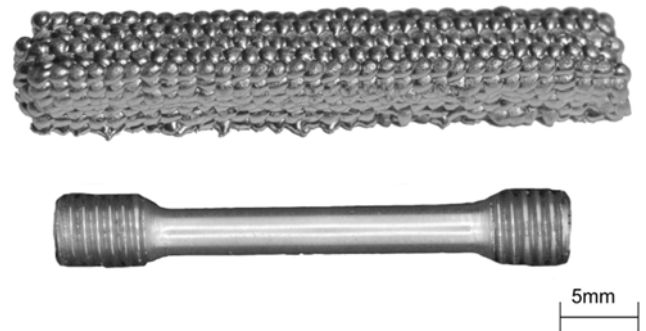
Gedruckter Quader und eine daraus gefertigte Zugprobe
